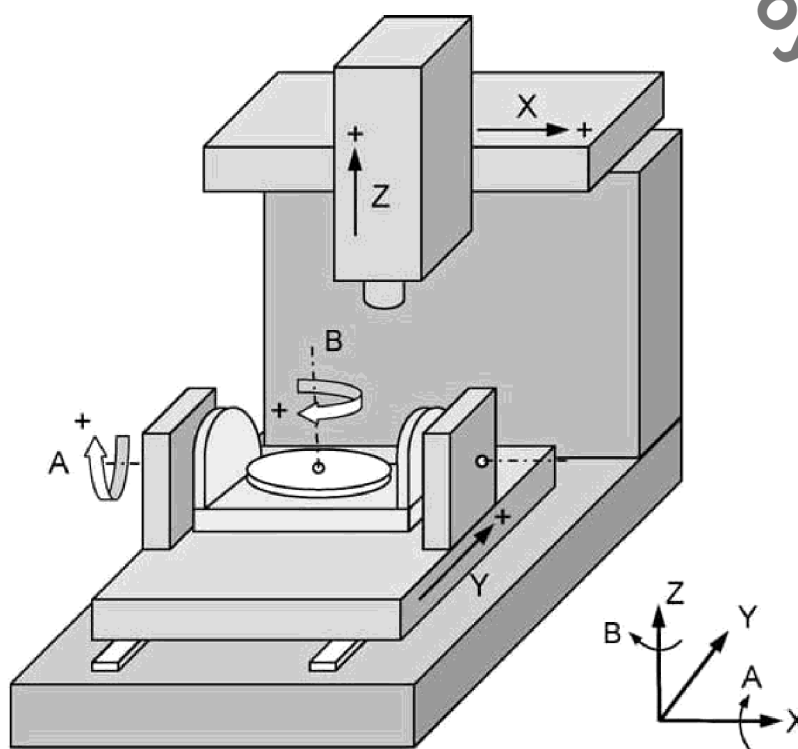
Розміщення 5-ти осей під час фрезерування
